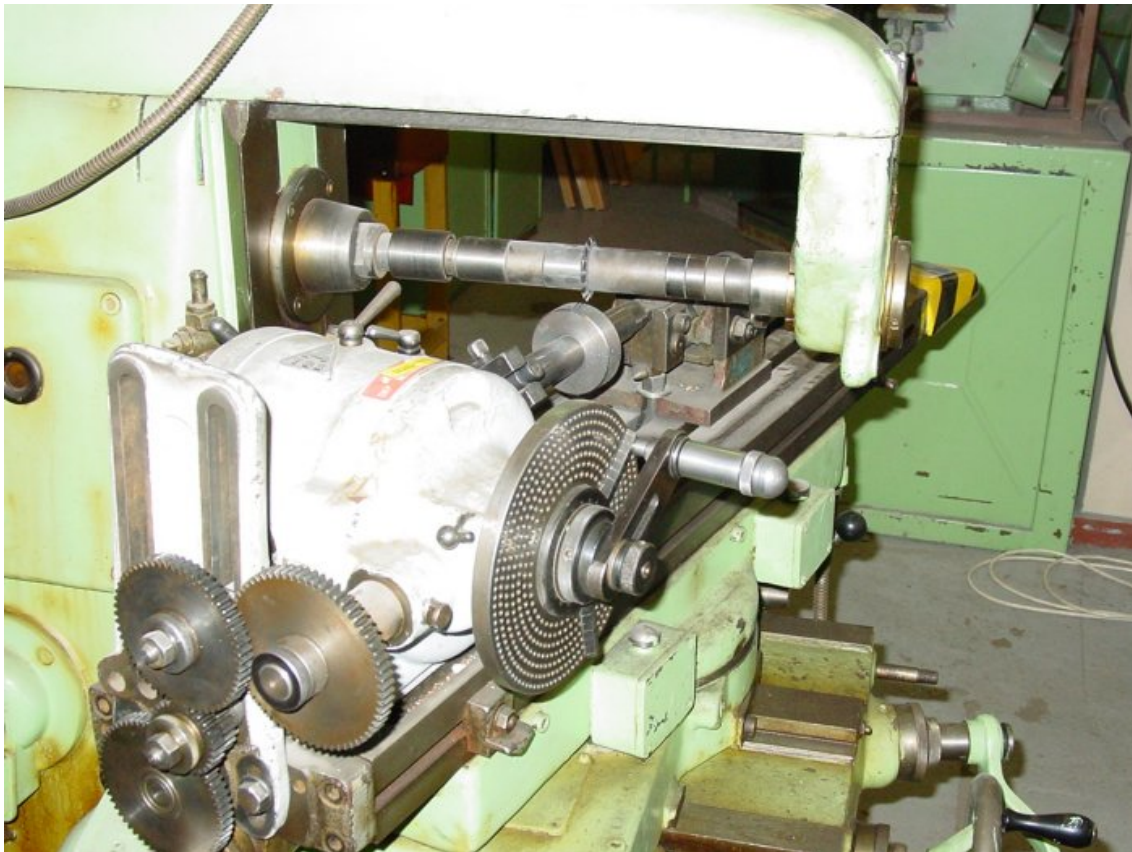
Frézování čelního ozubení dělicím způsobem kotoučovou frézou
